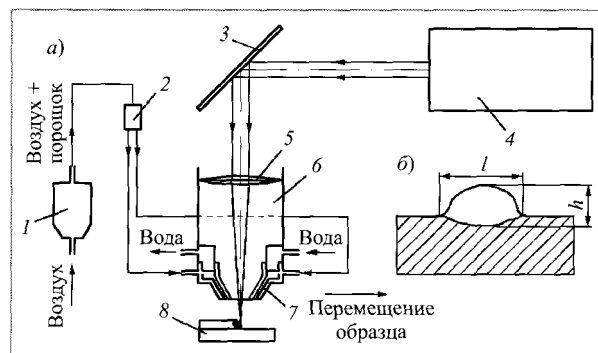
Схема лазерной наплавки (а) и размеры наплавленного валика (б):
